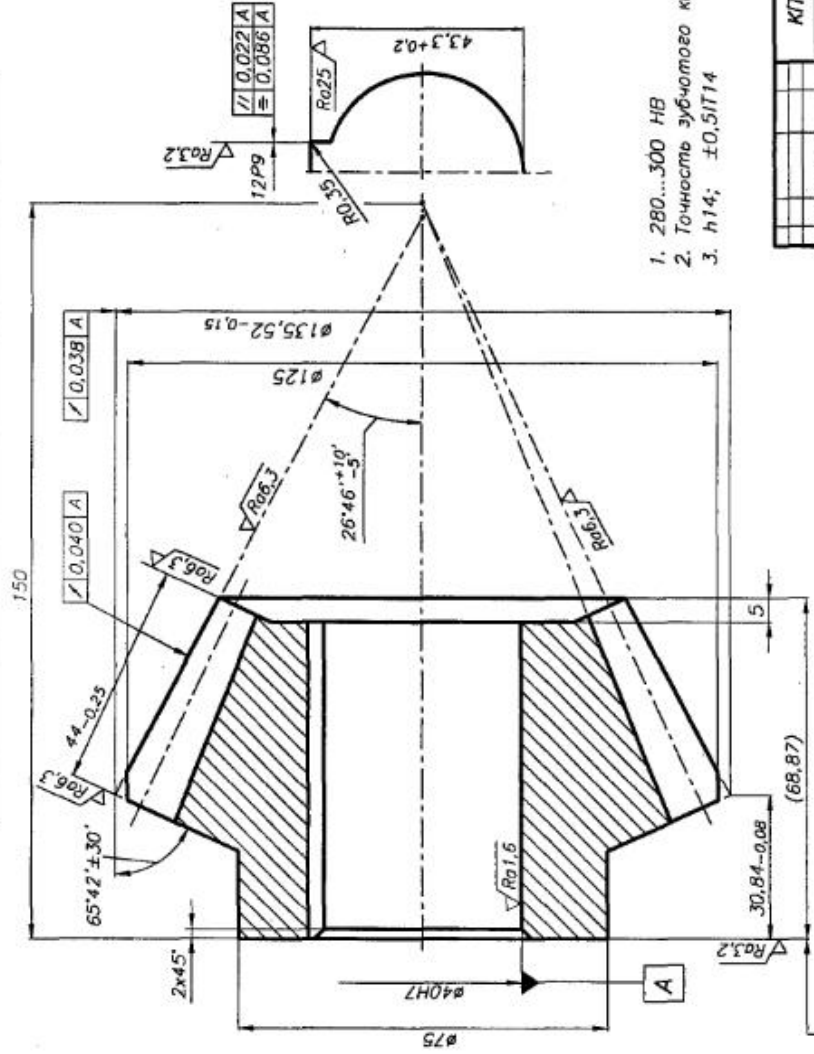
Допуски формы и расположения поверхностей для вариантов 1, 2, 3 выполнения заготовок конического колеса при различных базовых поверхностях для нарезания зубьев
